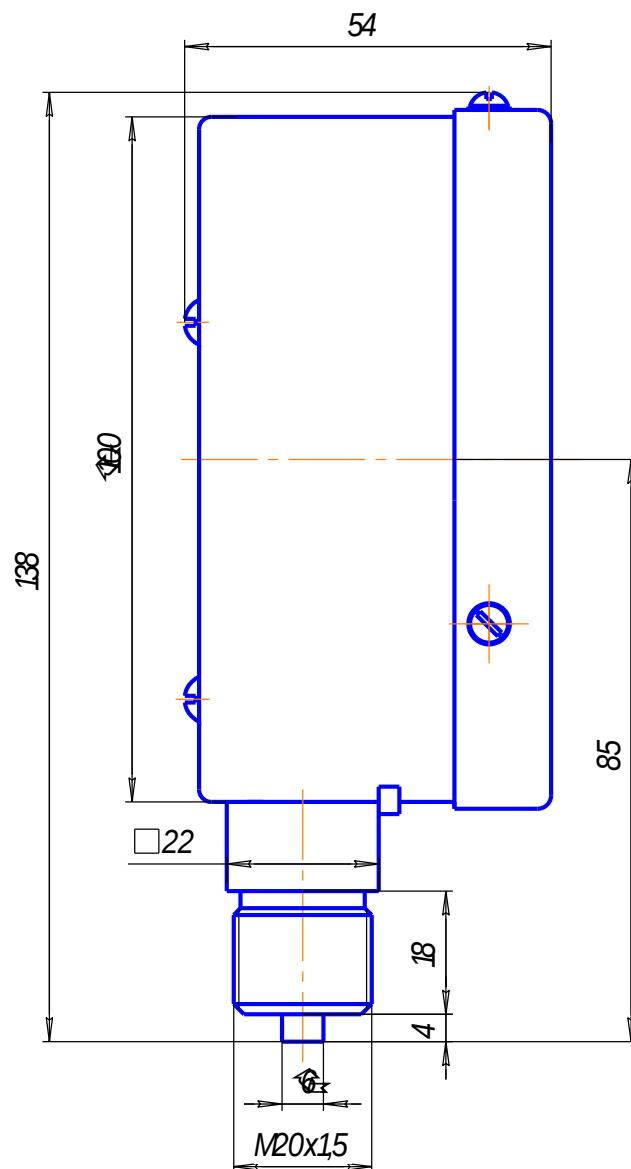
Габаритные и присоединительные размеры прибора с радиальным исполнением штуцера
